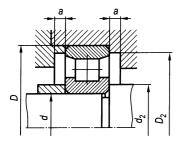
Примеры закрепления подшипников на валу, осях и в корпусе
